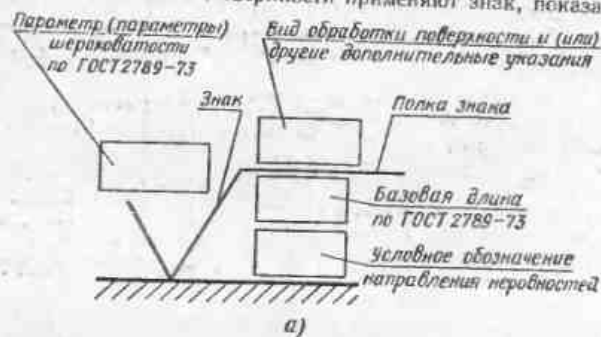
Структура обозначения и знака обозначения шероховатости поверхности
